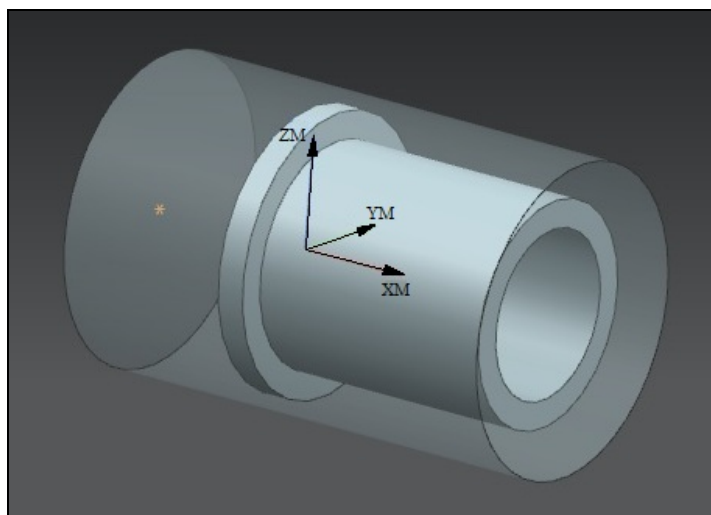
3D-модель детали после наложения на нее модели заготовки
